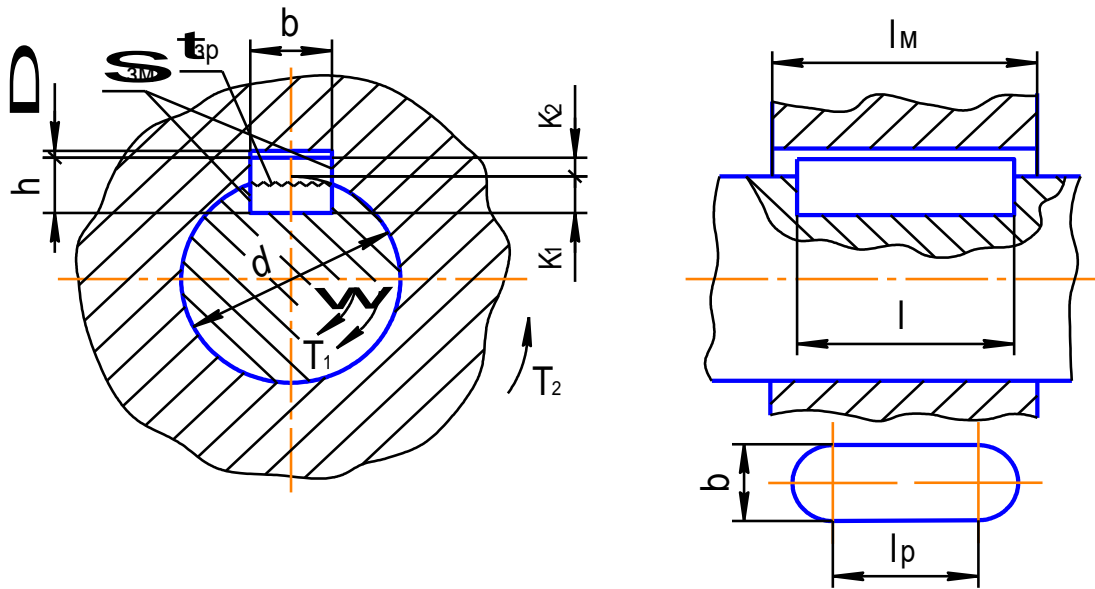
Конструкція шпонкового з'єднання з призматичною шпонкою
